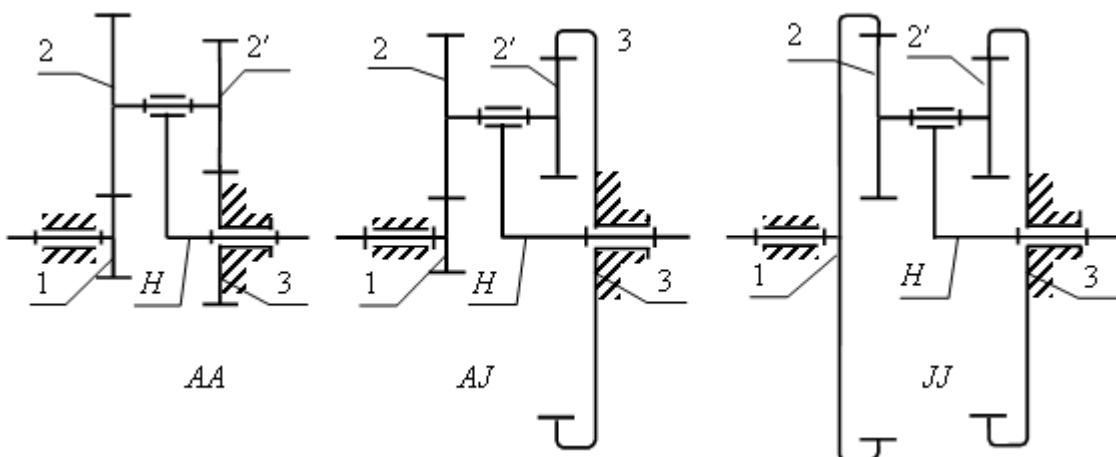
Типові схеми планетарних механізмів із циліндричними зубчастими колесами із здвоєним сателітом 2–2'
